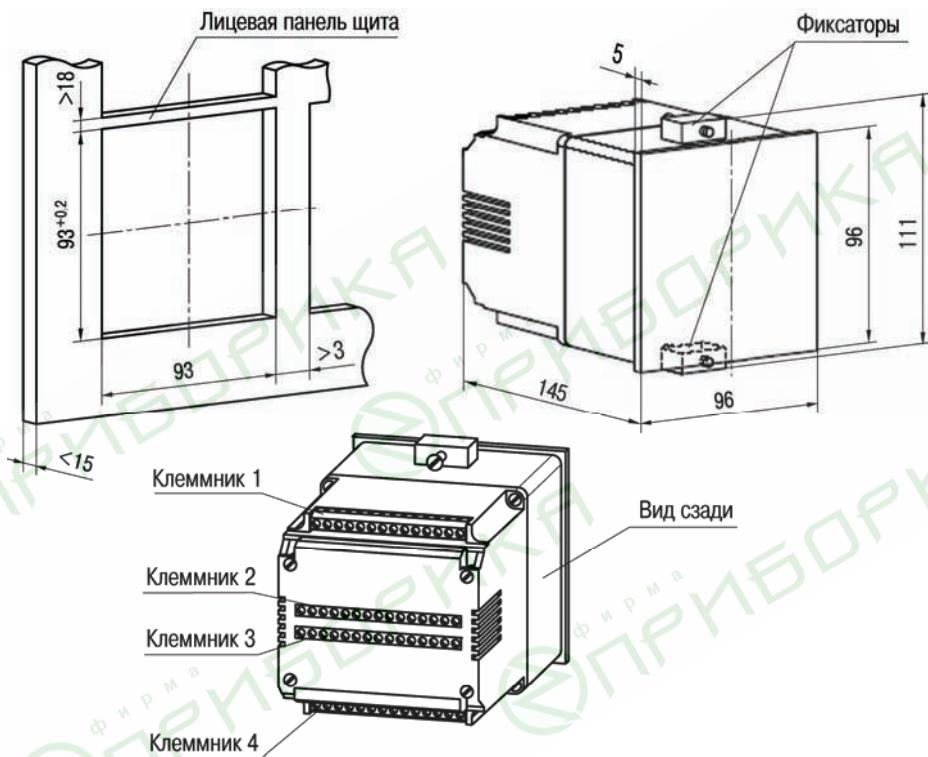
Габаритные и установочные чертежи прибора TPM148 щитового крепления
